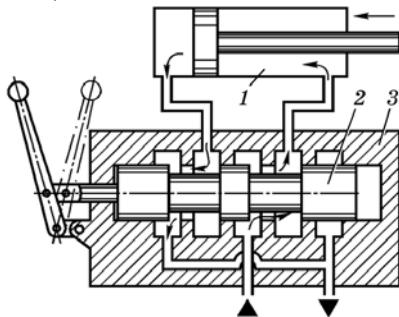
Схема роботи розподільника з циліндричним золотником: 1 — гідроциліндр; 2 — золотник; 3 — корпус
